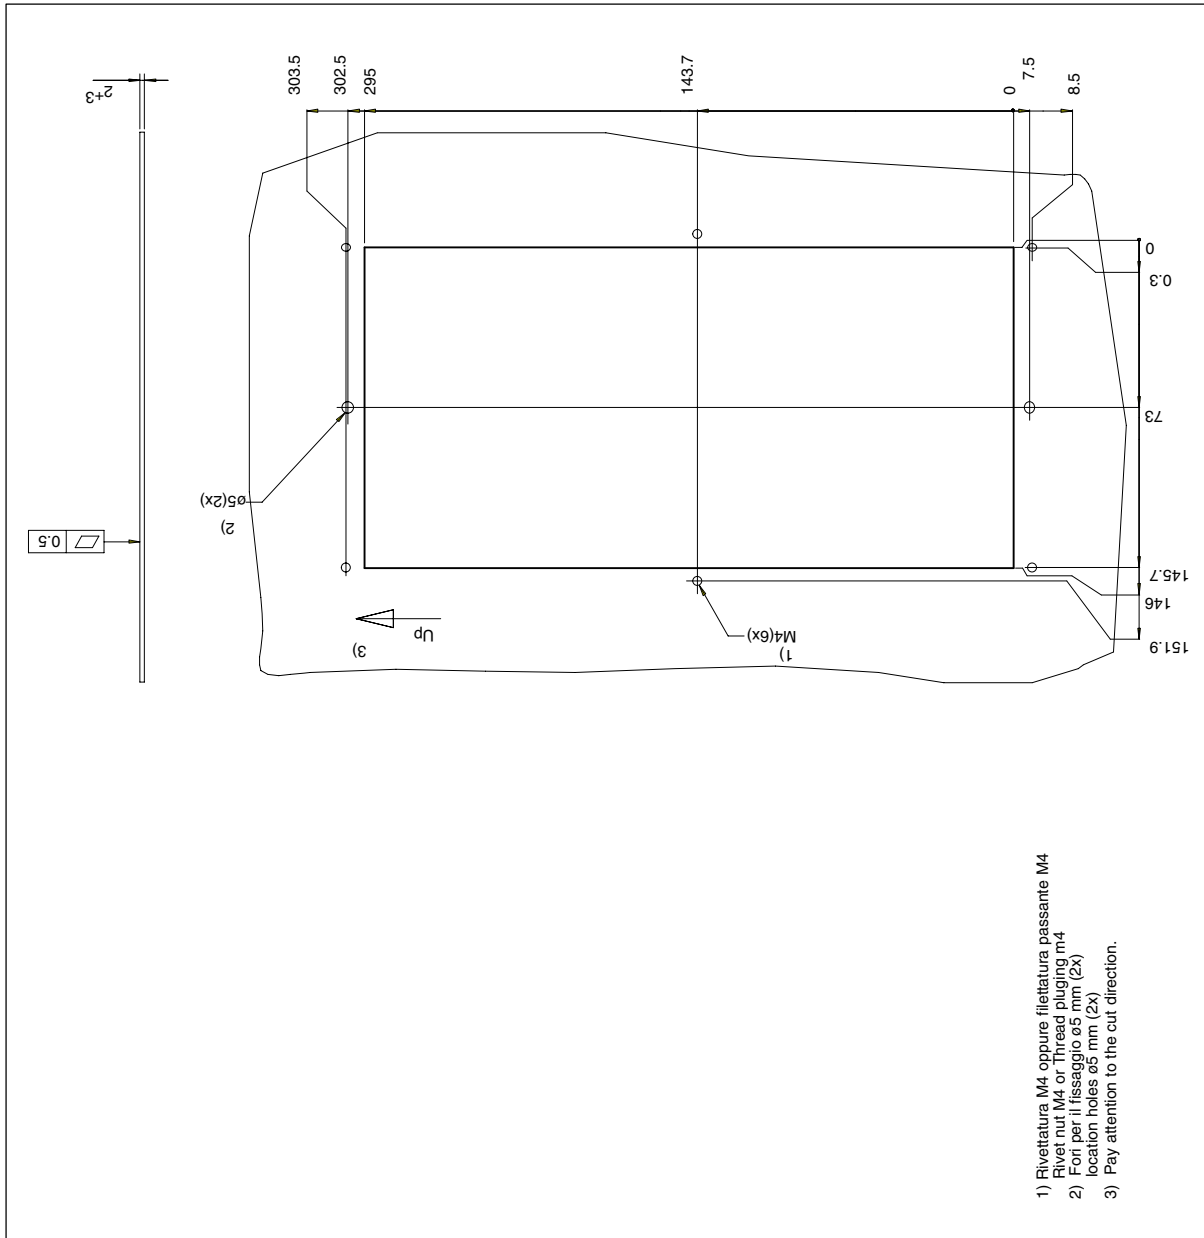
Dima di foratura Keyboard (layout verticale per il montaggio a fianco della PCU)
